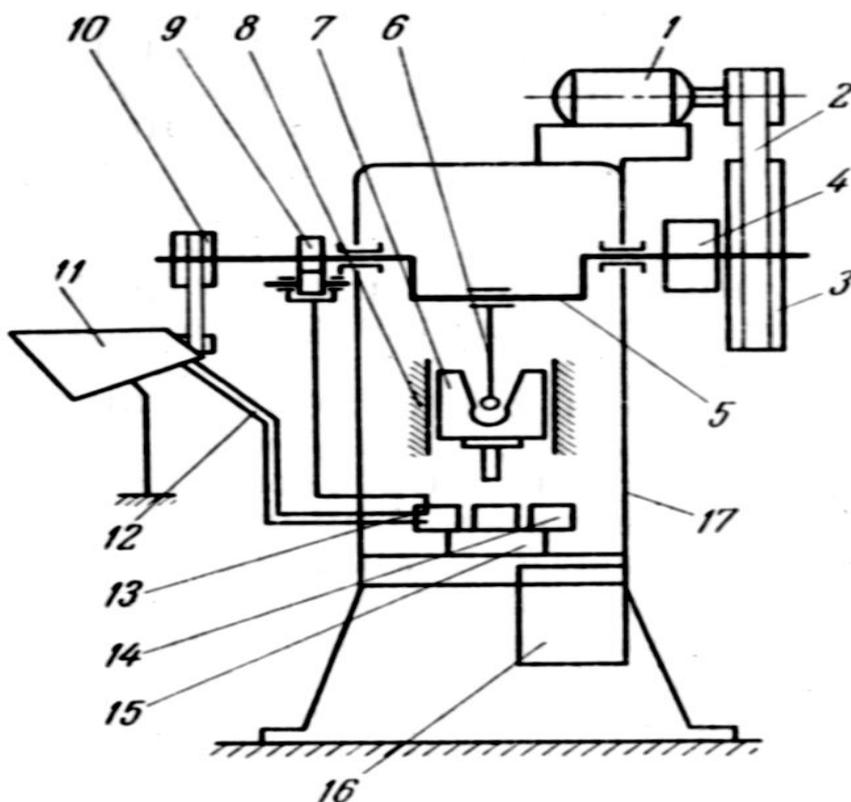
Схема кривошипного пресса: 1 — электродвигатель; 2 — передача привода; 3 — маховик; 4 — муфта включения; 5 — кривошипный вал; 6 — шатун; 7 — ползун; 8 — направляющие; 9 — привод питателя; 10 — привод автоматического бункерного захватного устройства; 11 — автоматическое бункерное захватно-ориентирующее устройство; 12 — магазин-накопитель; 13 — питатель; 14 — устройство, удаляющее отходы; 15 — устройство, удаляющее и стапелирующее изделия; 16 — система управления; 17 — станина
